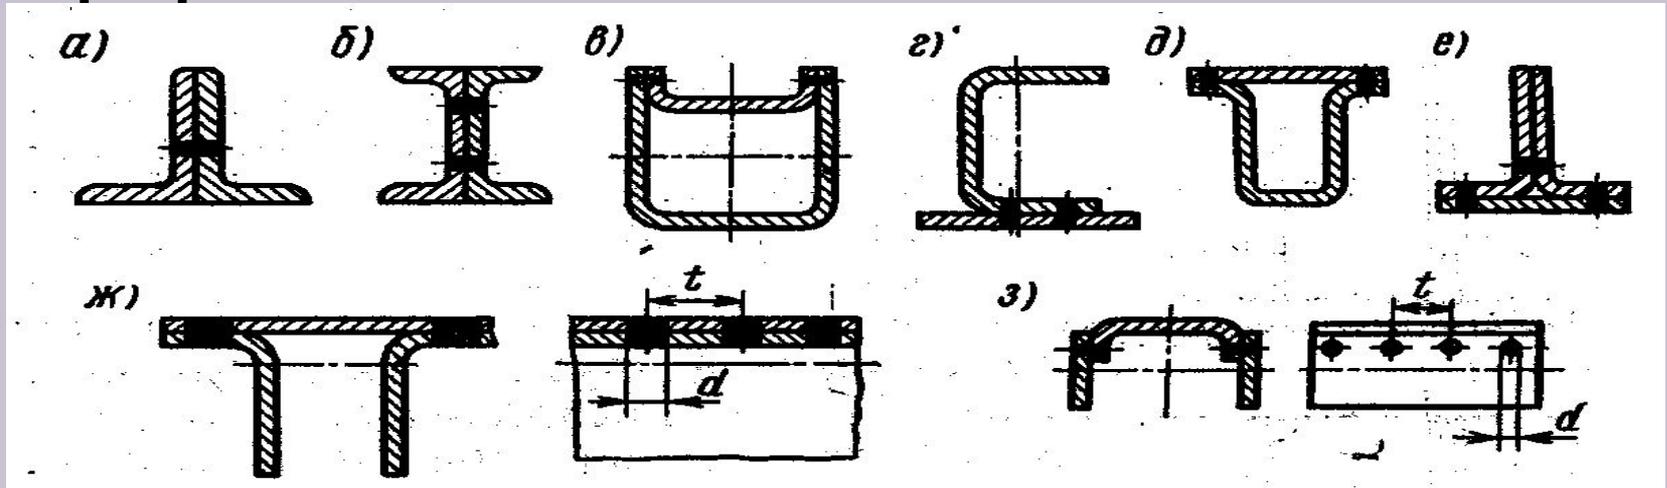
Примеры поперечных сечений балок, сваренных точечной сваркой:
